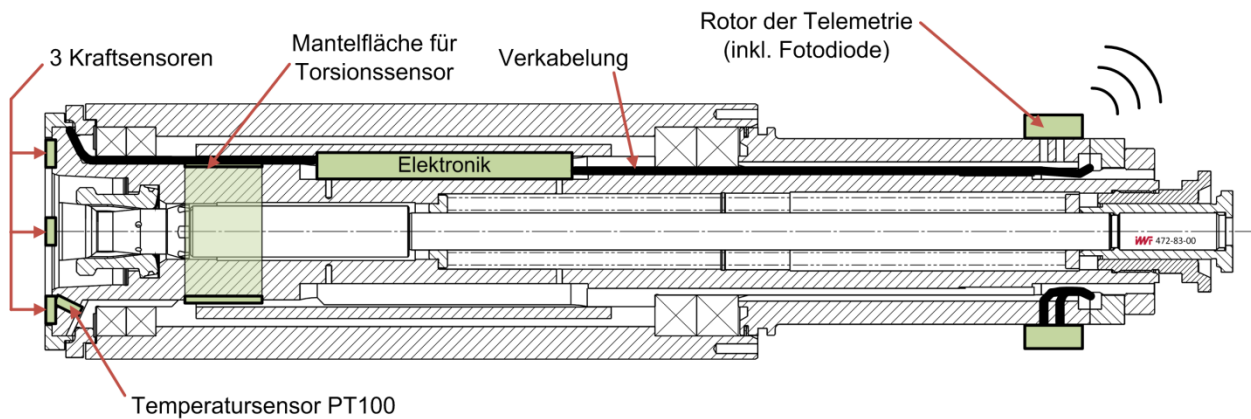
Sensorintegrierte Werkzeugspindel für Hobel- und Kehlmaschinen
